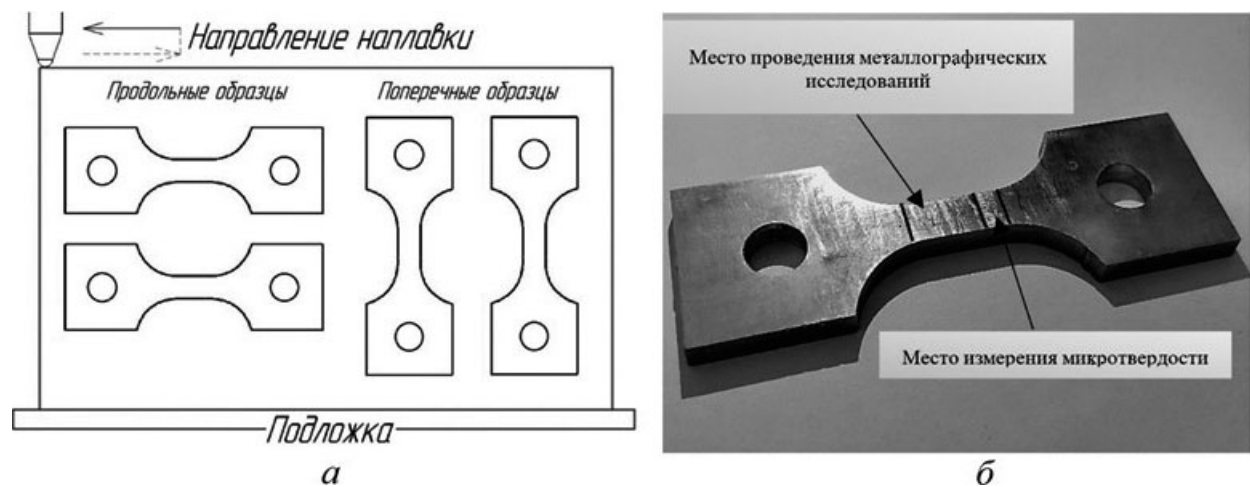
Схема вырезки образцов из наплавленной стенки (а) и их внешний вид с исследуемыми зонами (б)
